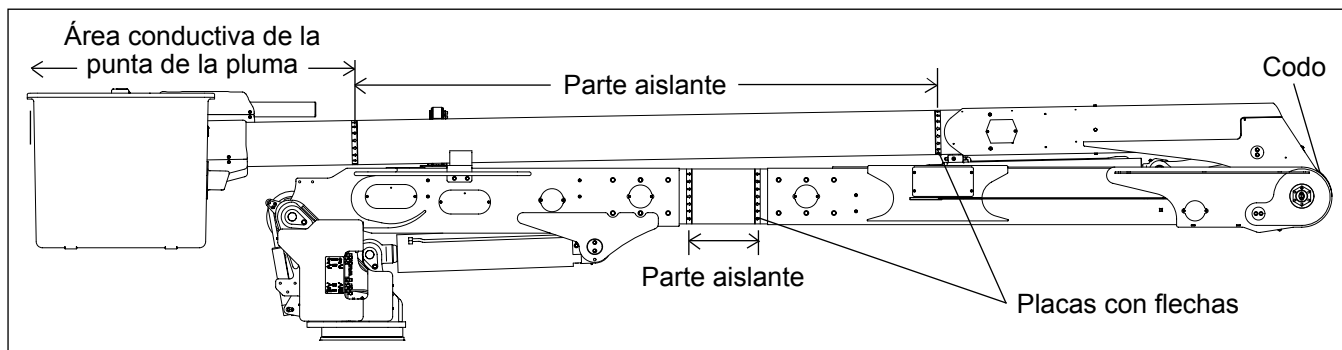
Parte aislante de las plumas y área conductiva de la punta de la pluma
